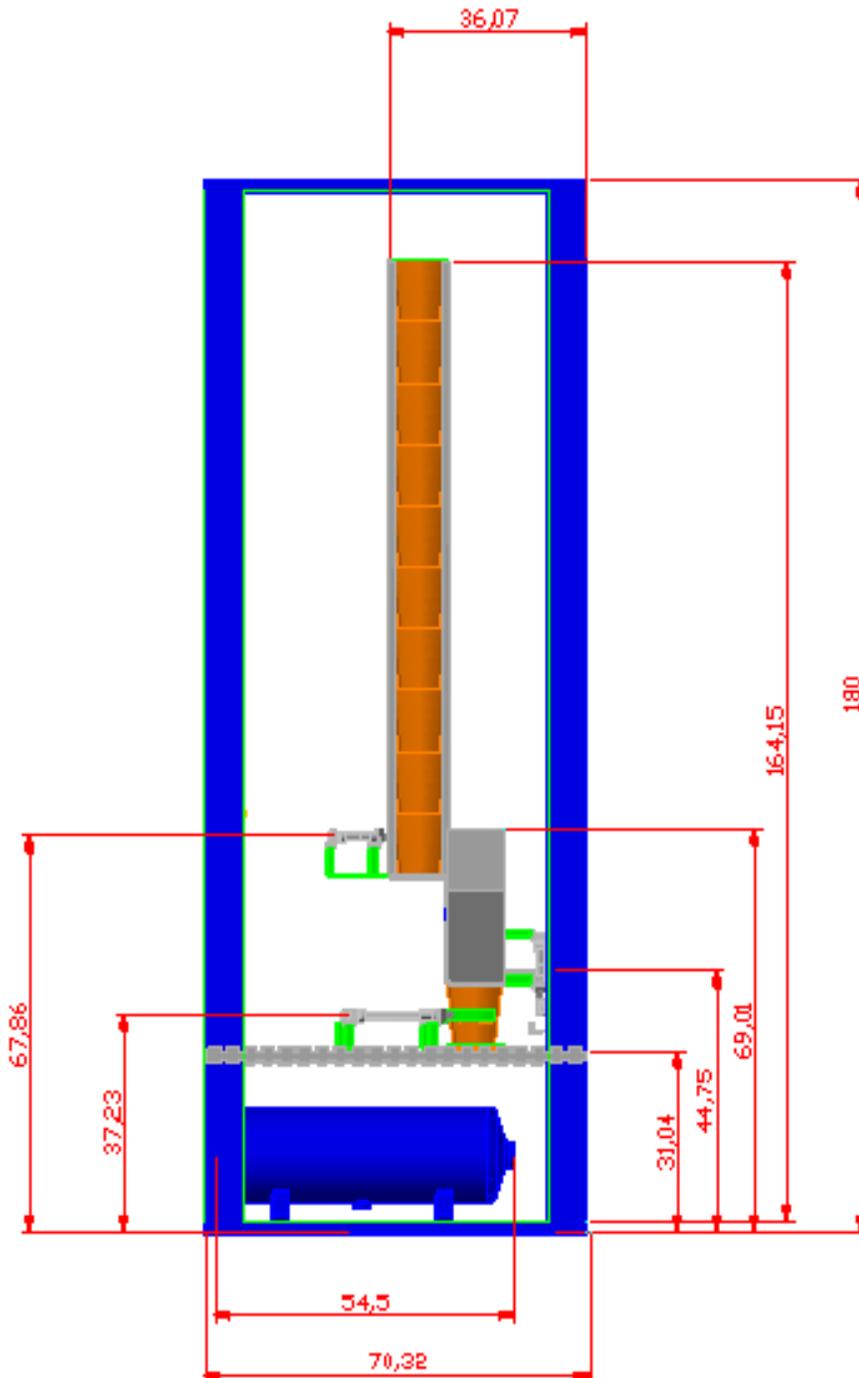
Dimensiones del sistema vista lateral.
